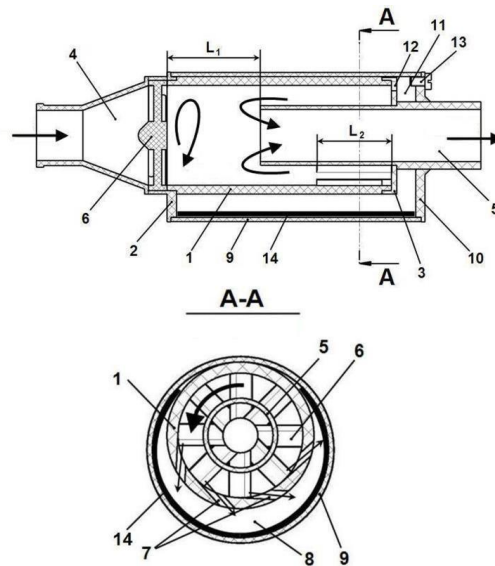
Пристрій для очищення охолоджувальної рідини: 1 – циліндричний корпус; 2, 3 – торцеві стінки, виконані у вигляді фланців; 4 – вхідний патрубок; 5 – вихідний патрубок; 6 – закручувальний апарат; 7 – щілини для відведення частинок забруднень; 8 – грязезбірник; 9 – циліндричний кожух; 10 – додатковий фланець; 11 – кільцева камера; 12 – дренажний отвір; 13 – різьбова пробка; 14 – вставка у формі тонкого листа з магнітопластику [1].
